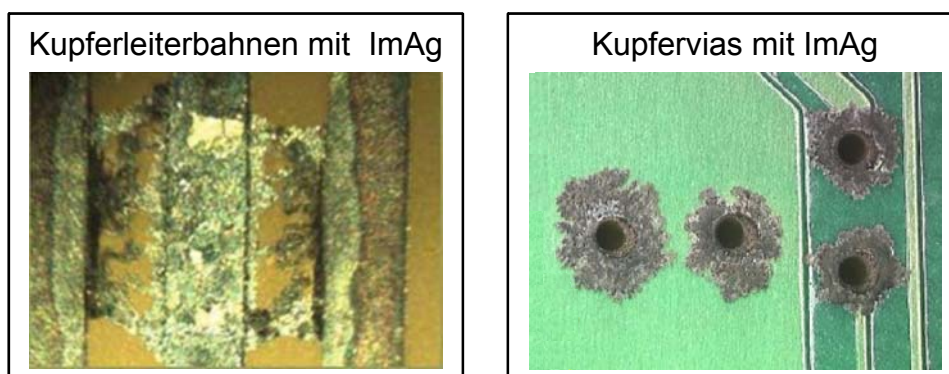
Kriechkorrosion auf Kupferleiterbahnen mit chemisch versilberter Oberfläche
